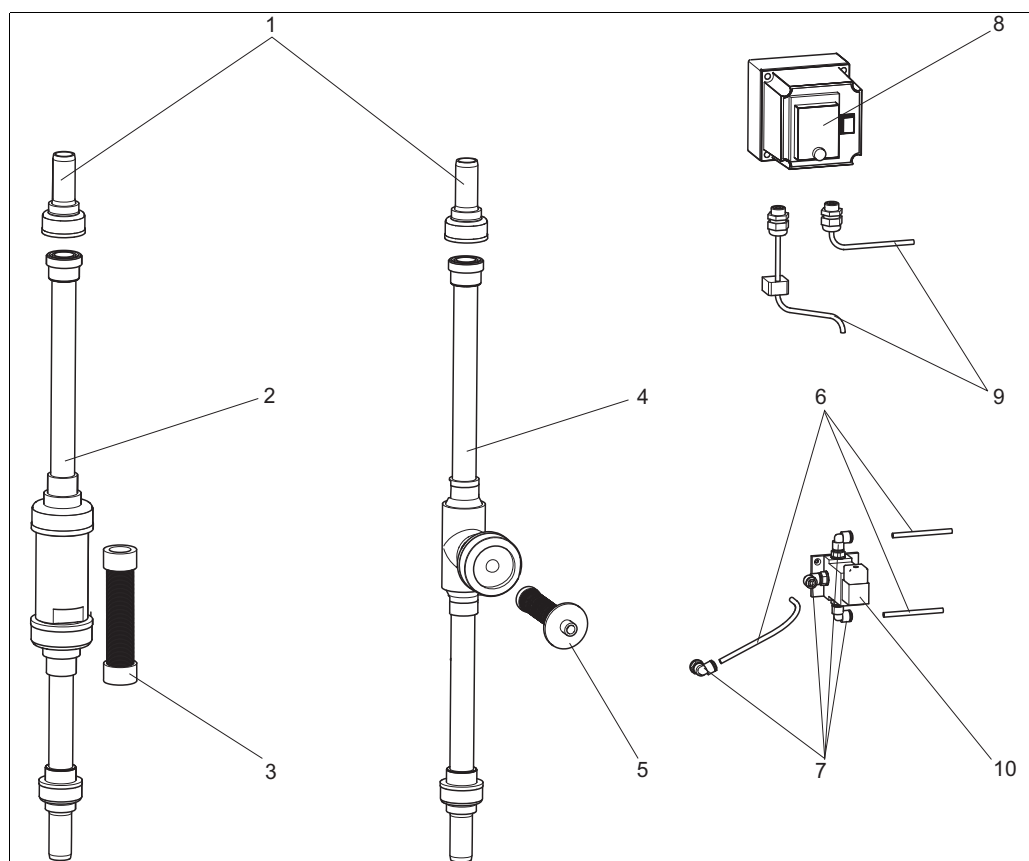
CAT221 : toutes les versions (sans boîtier ou plaque de montage)
